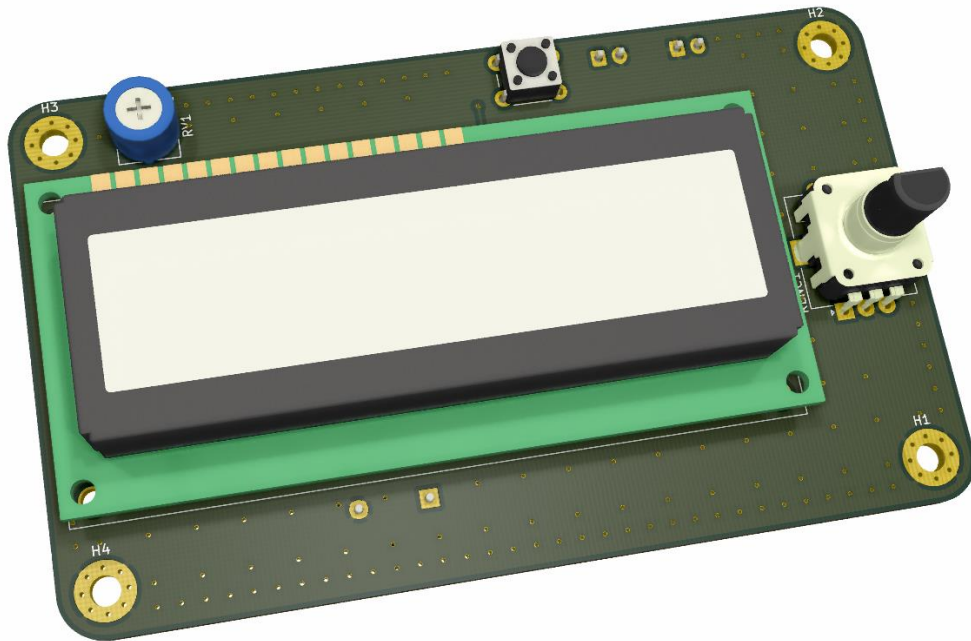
vue 3D de la carte de commande de la soudeuse par point
